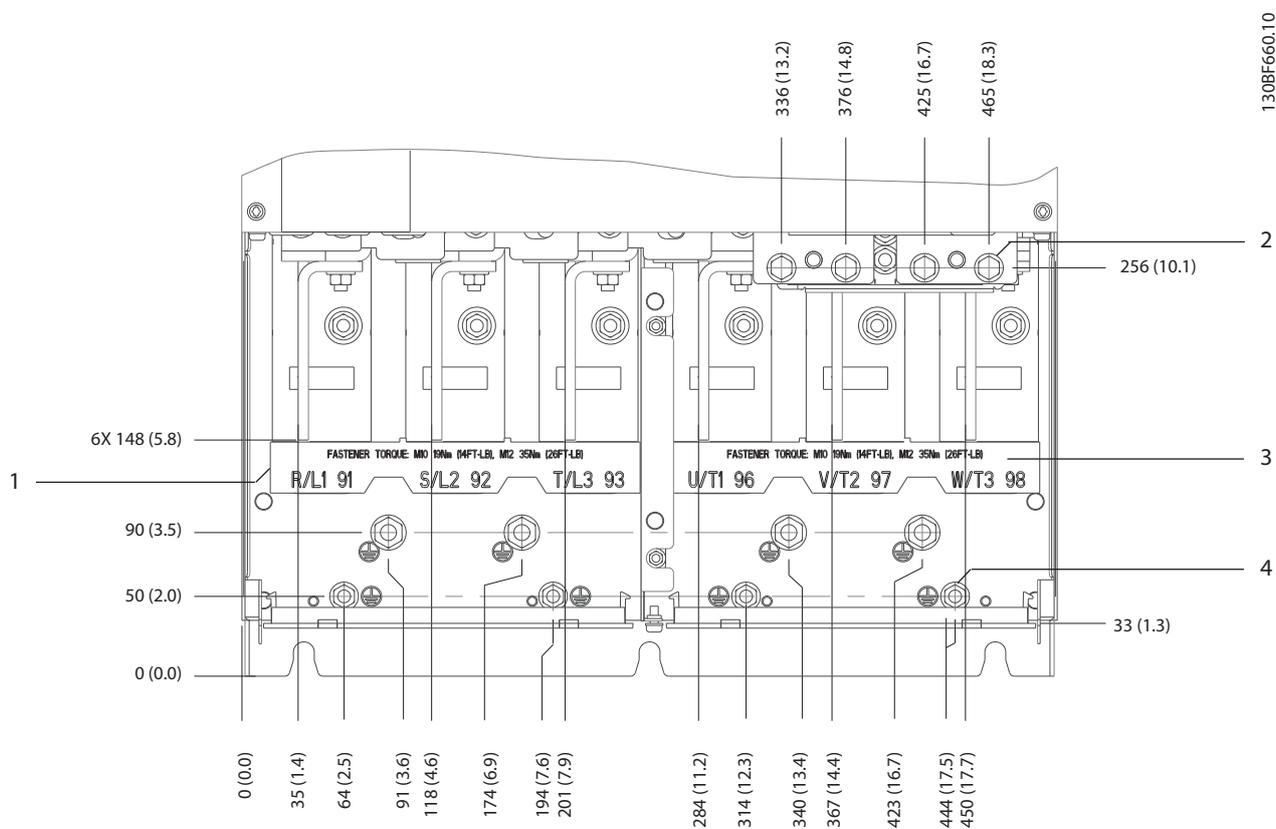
Dimensions des bornes E2h (vues latérales)
